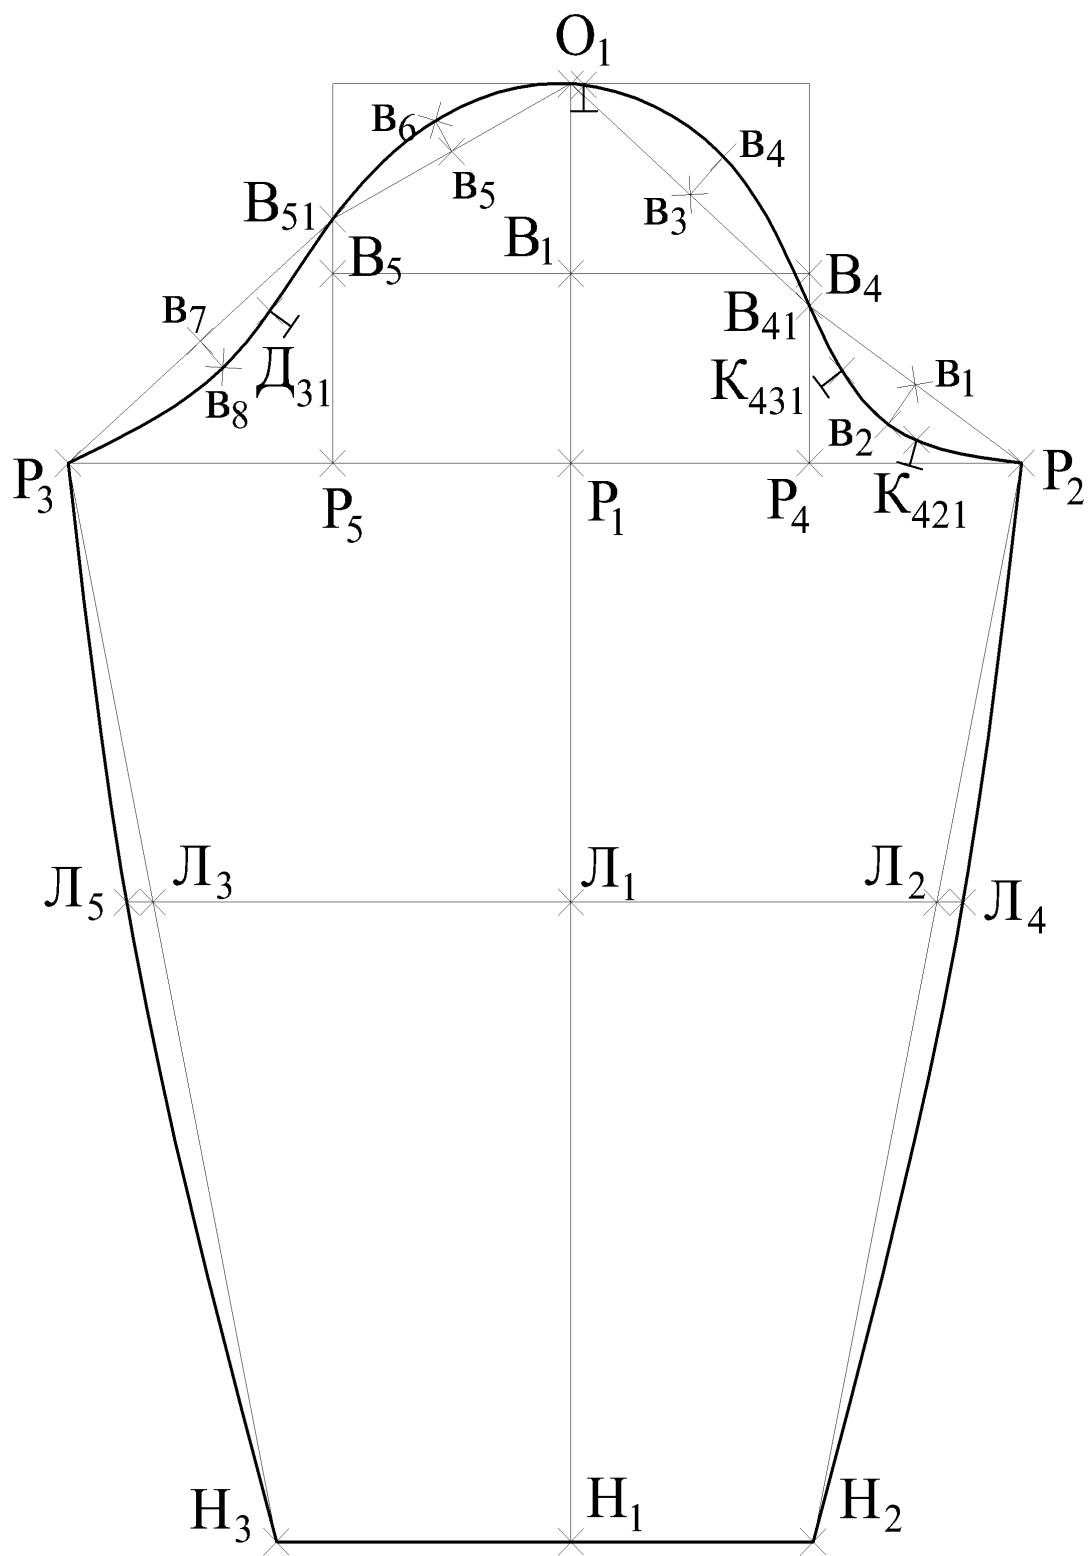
Чертежи сетки размеров и конструкции рукава джемпера полурегулярного
